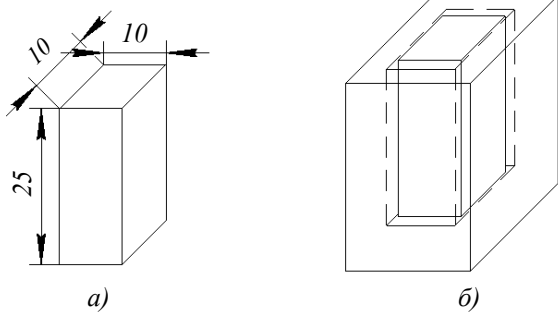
Форма и размеры образца (а), и расположение его в оправке (б)
